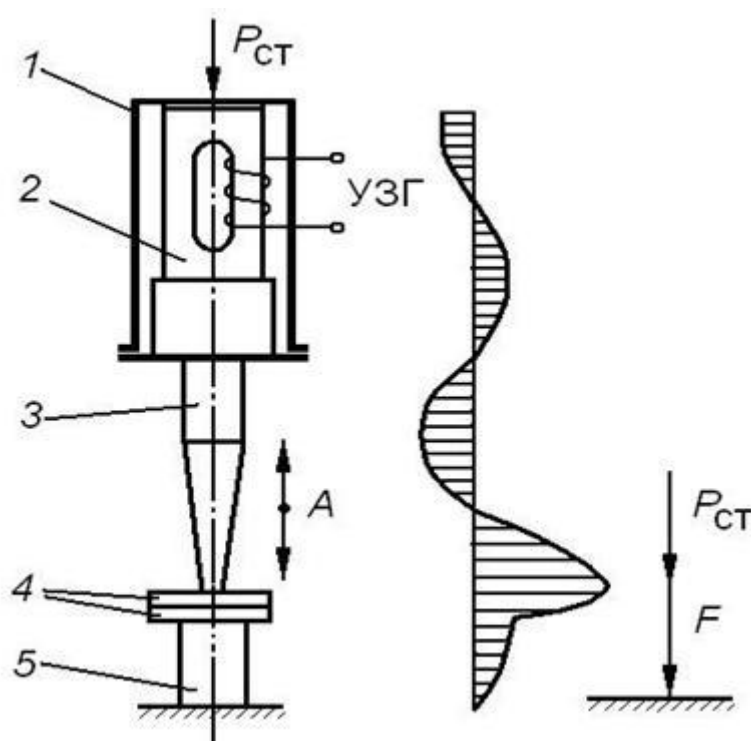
Схема ультразвукового зварювання пластмас: 1 – корпус перетворювача; 2 – перетворювач; 3 – трансформатор – хвилевід; 4 - деталі, що зварюються; 5 – опора.
